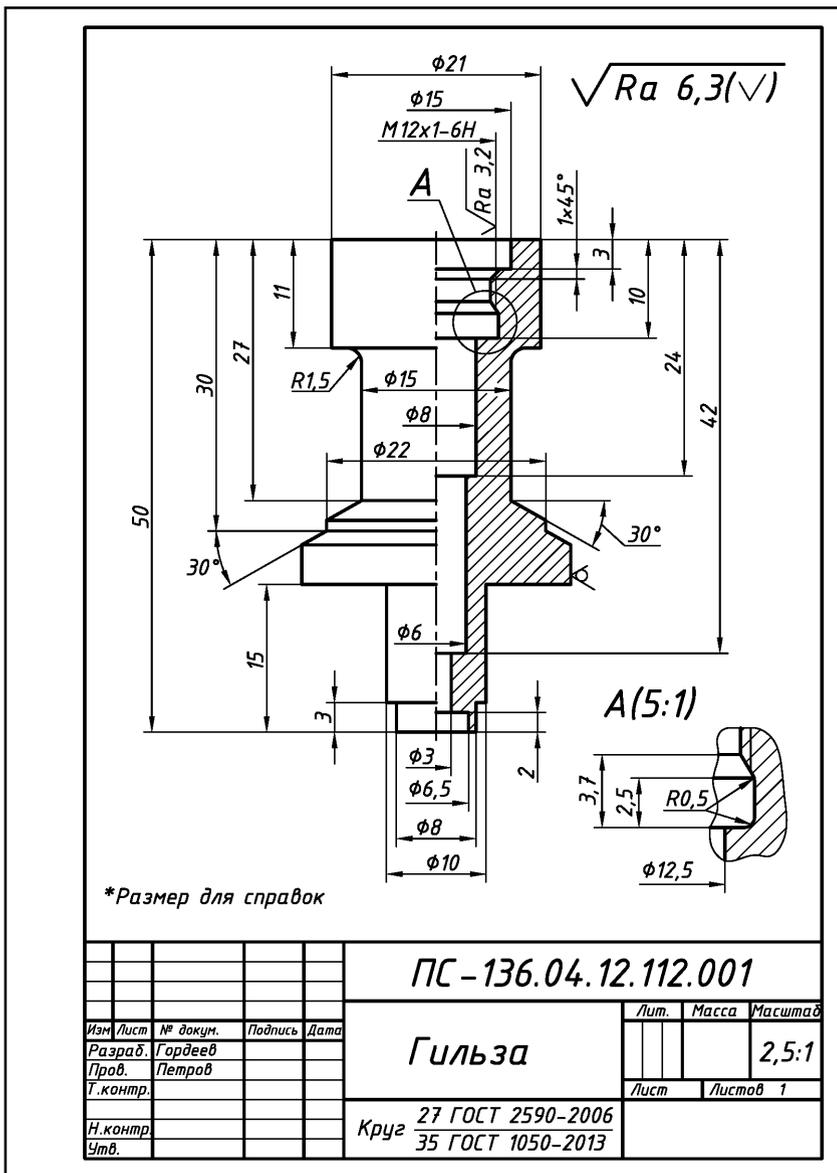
Оформление рабочего чертежа точеной детали из металла
